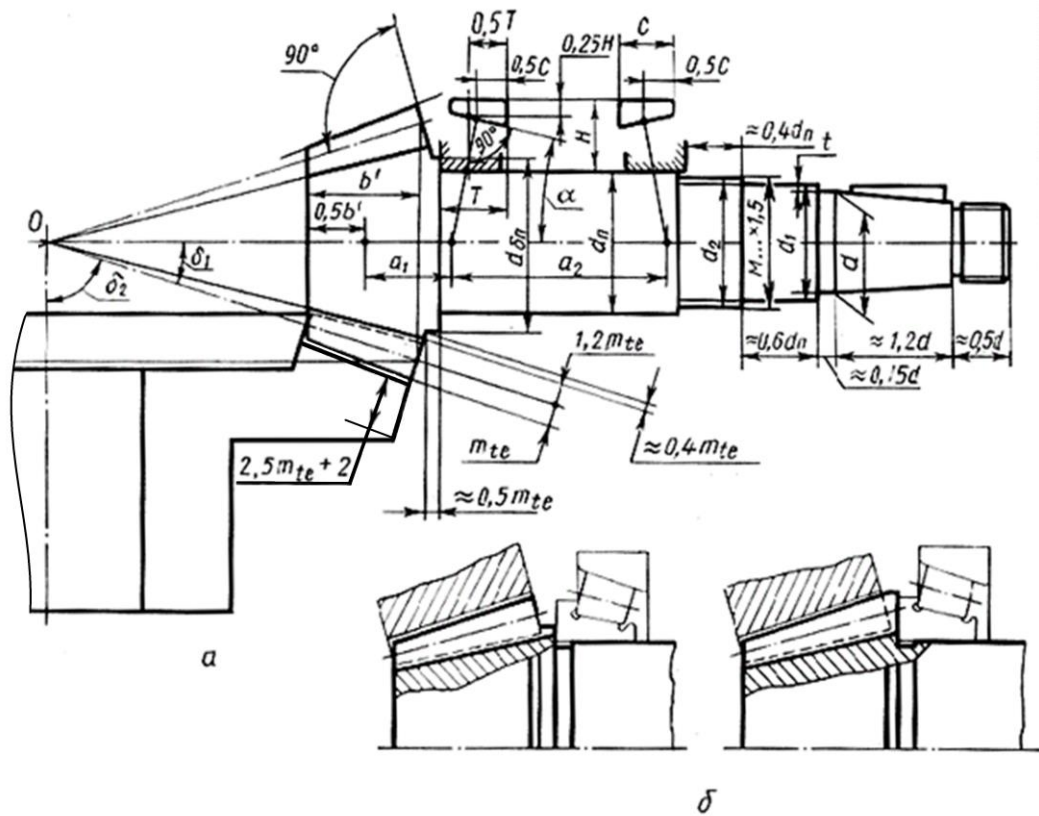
Соотношение размеров вала для конической вал-шестерни:
